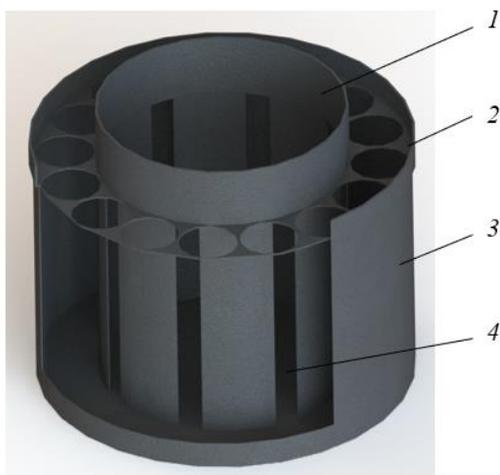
Трехмерная модель центробежного сепарационного устройства с соосно расположенными трубами (вид с разрезом): 1 – входной патрубок внутренней цилиндрической трубы, 2 – решетка с круглыми отверстиями, 3 – корпус сепарационного устройства, 4 – прямоугольные щели
